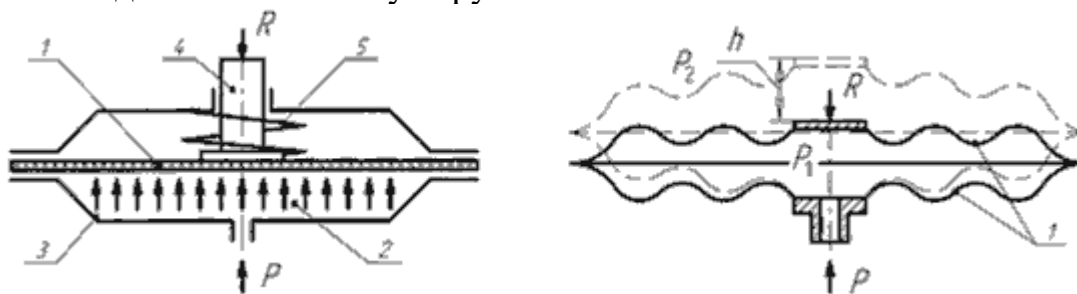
Схеми мембран: а - плоска з еластичним кільцем; б - гофрована металева
